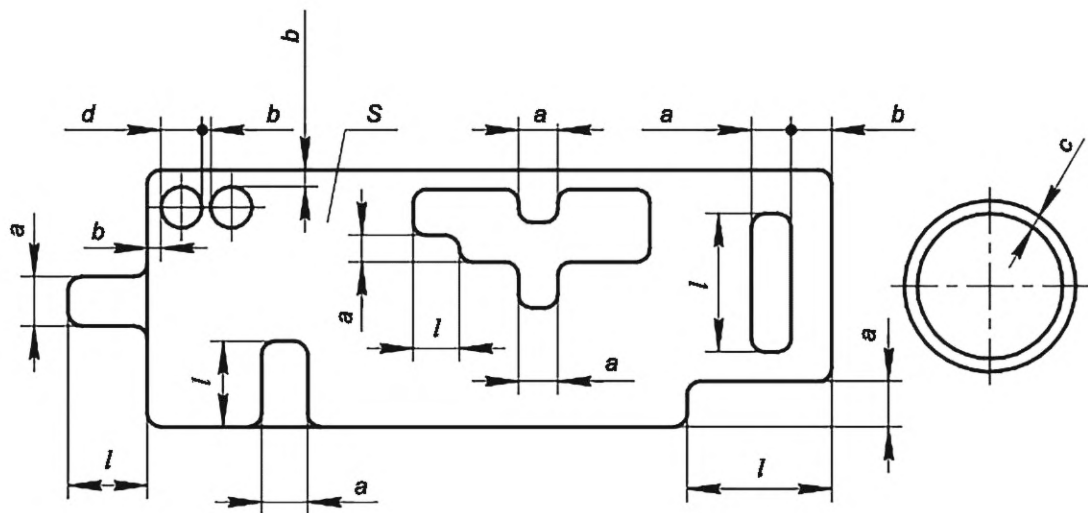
Размеры отверстия, перемычки, выступа, впадины, паза и кольца
